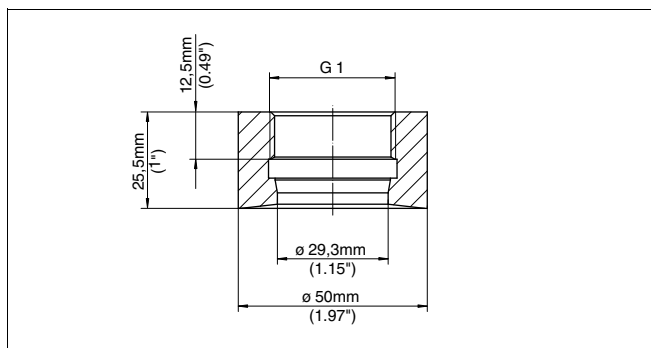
Размеры приварного штуцера G1, гигиеническое присоединение
